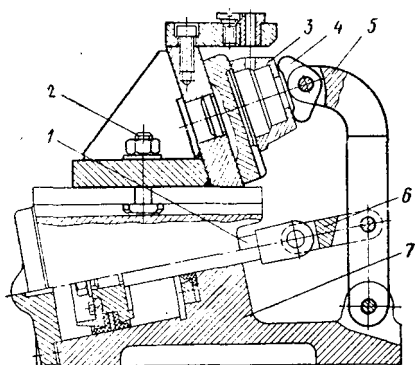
Универсально-наладочное приспособление для групповой обработки отверстий в крышках подшипников
